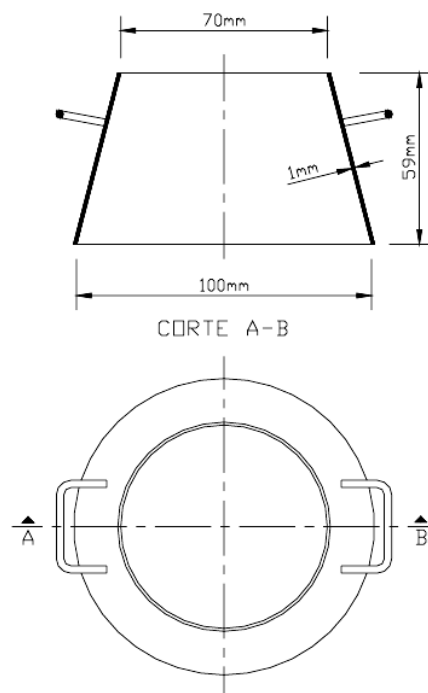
Dimensões do cone de espalhamento em argamassas [46]
